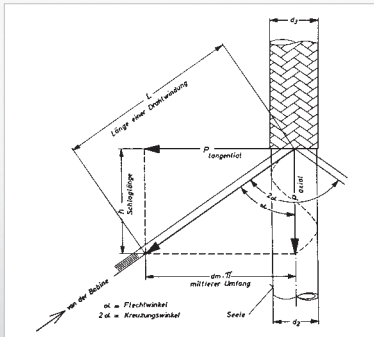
Geometrie des Schlauchgeflechtes
